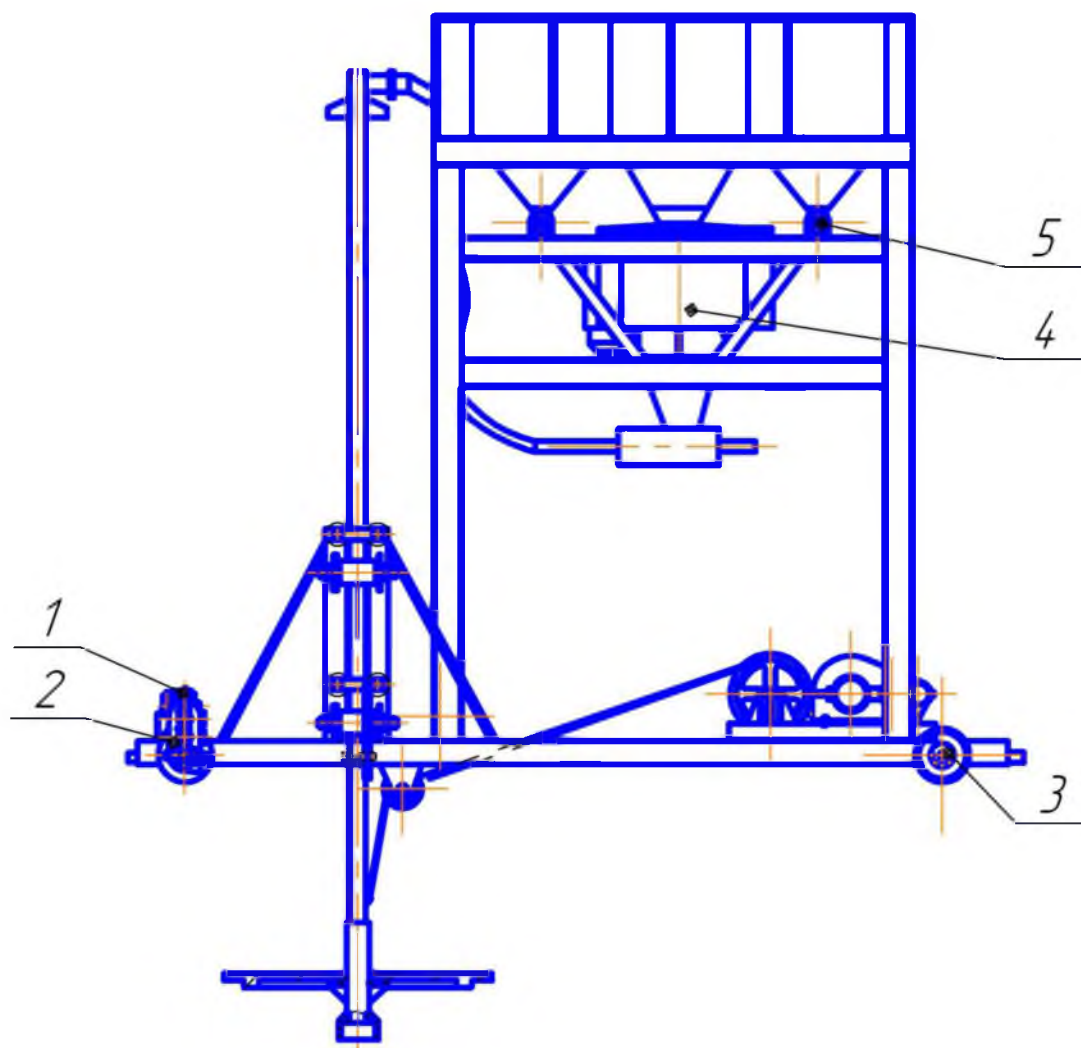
Схема точок змащування установки для обробки чавуну
